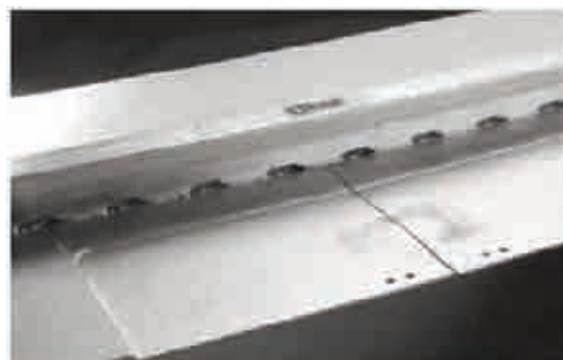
Испытательный образец Y-стрингера с выемками (Mouse holes)
